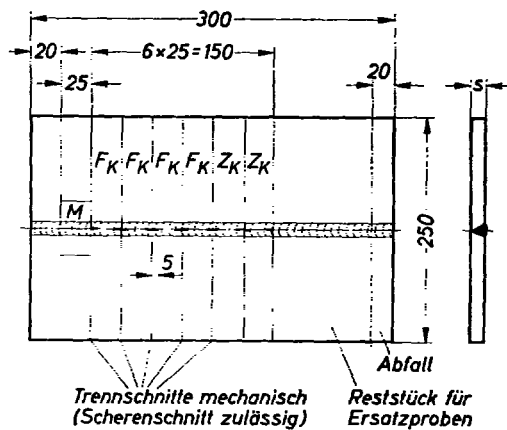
Stumpfnahtrprüfstück für Blechschweißer an $s = 1,5$ bis 2 mm (Probenlage schematisch eingezeichnet)
